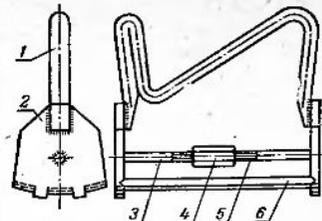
Напильник для обработки планок подбаранья зерноуборочного комбайна:
